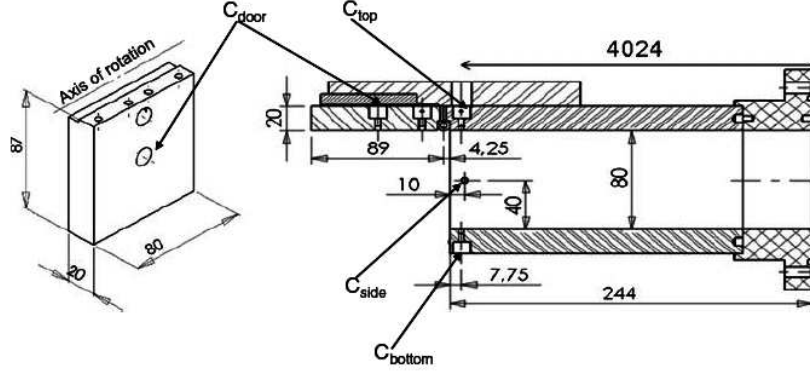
Schéma de la porte à l'extrémité du tube à choc (repris de [12]). Les dimensions sont données en mm
